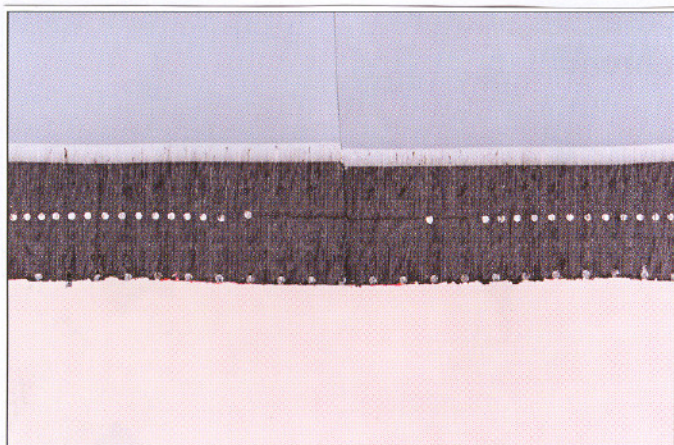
Схема сварки с помощью фитингов с закладным электронагревателем.
